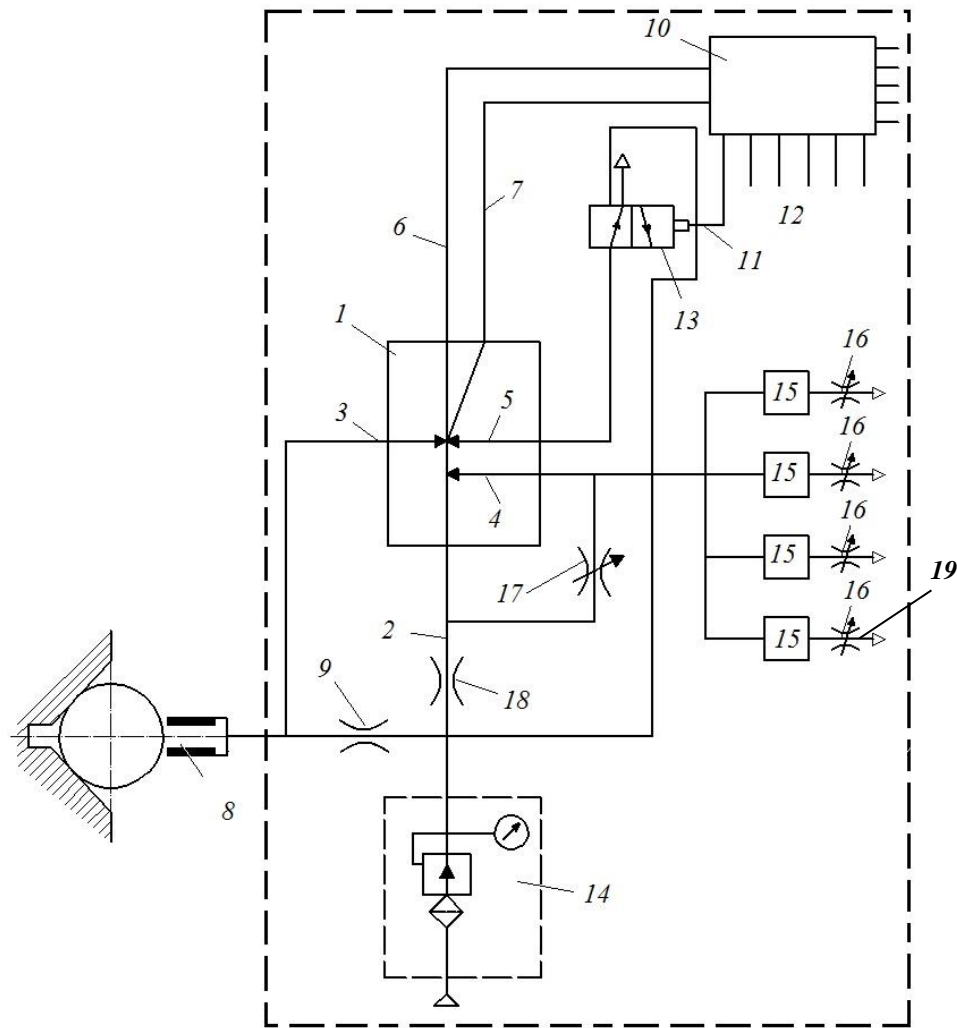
Устройство для контроля и сортировки деталей по линейным размерам:
